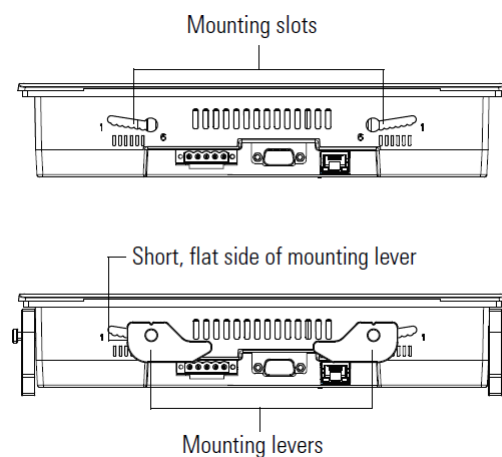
Detalle de las palancas de montaje y su ubicación (Fuente: propia)
